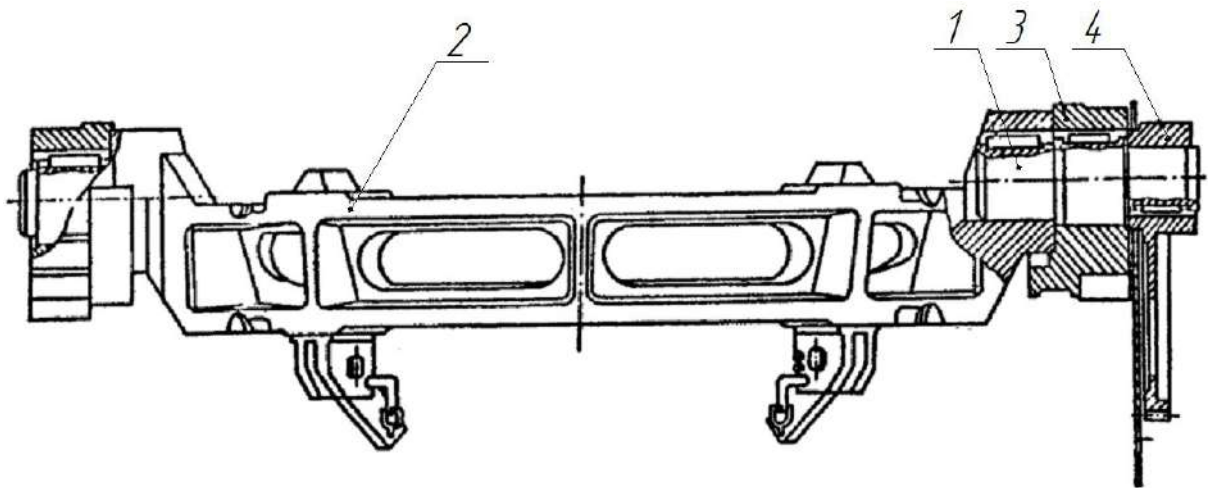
Загальний вид існуючої конструкції шлаковоза ШТД-16,5
